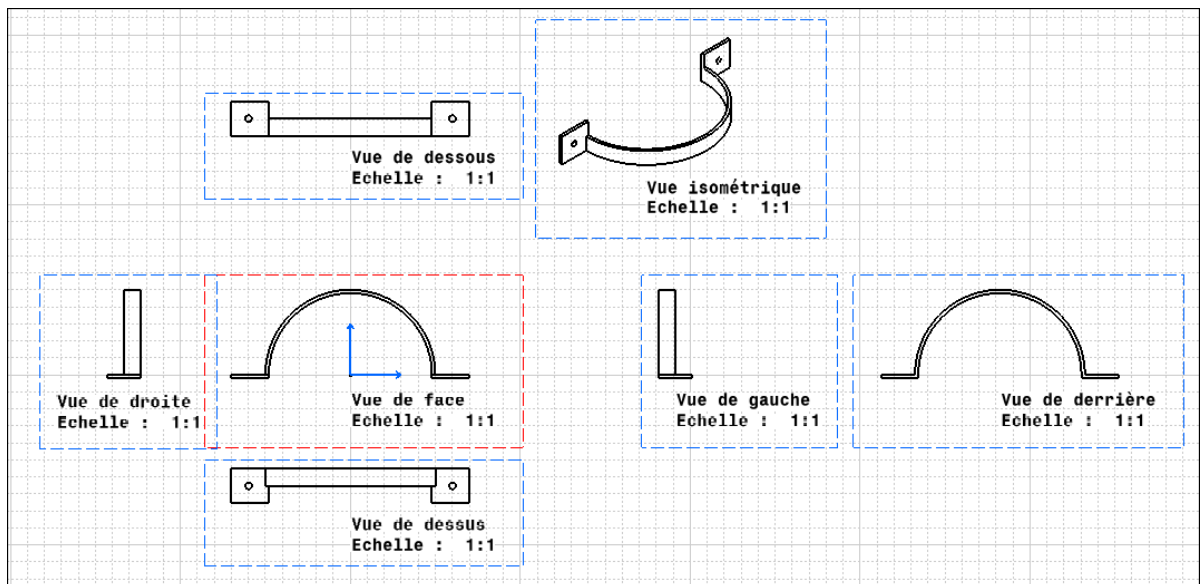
mise en plan de pièce de fixation de Kinect
